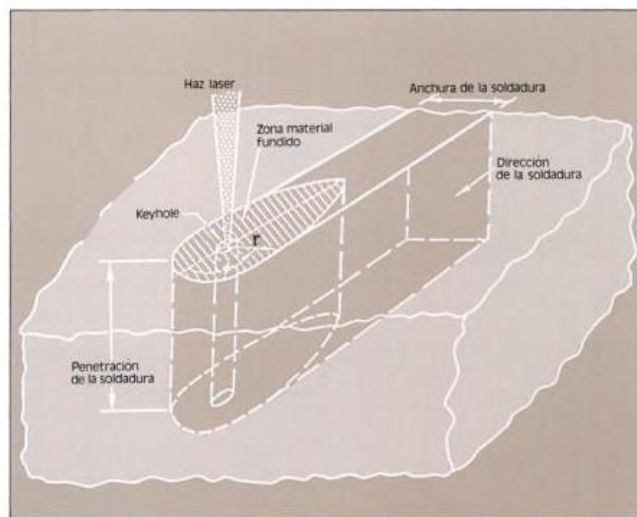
Mecanismo soldadura Laser. (Bachs & Cuesta, 1988)
